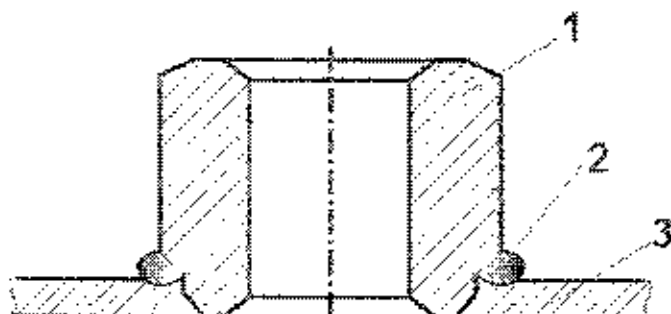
Увеличение длины свинчивания при помощи приваривания втулки: 1 – втулка; 2 – сварной шов; 3 – заготовка [3]
